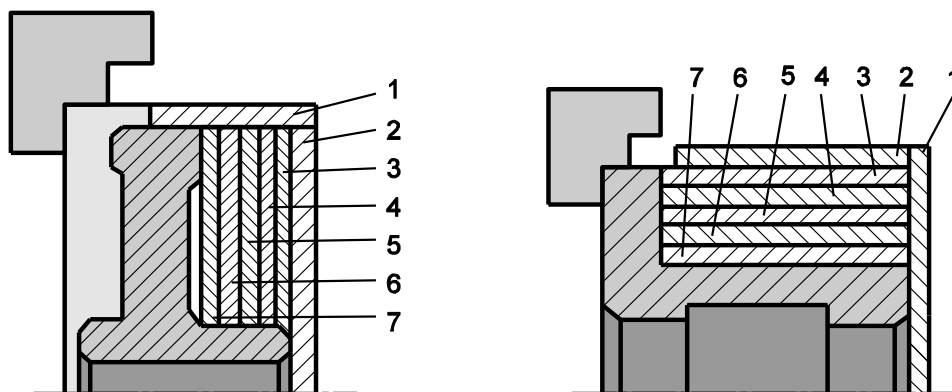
Обработка в патроне заготовок из проката:
